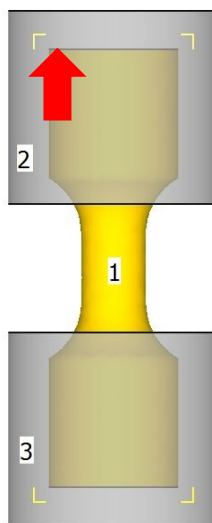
Сборка 3D моделей оснастки и заготовки для моделирования процесса растяжения: 1– заготовка; 2 – верхний держатель; 3 – нижний держатель.
